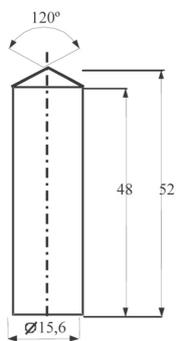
pistón cilíndrico de bronce, dimensiones en mm.
